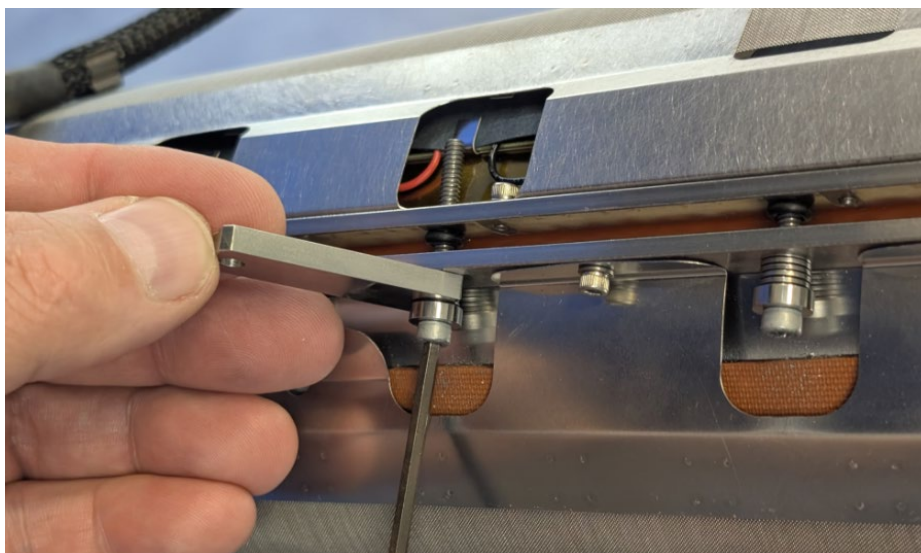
Приспособление для установки зазора стяжного ХОМУТА, установленное на винте
